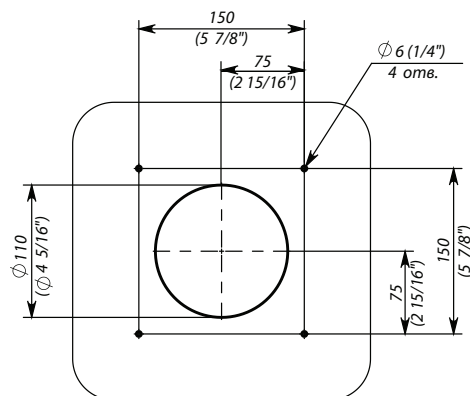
Схема разметки отверстий под крепеж блока вентилятора
